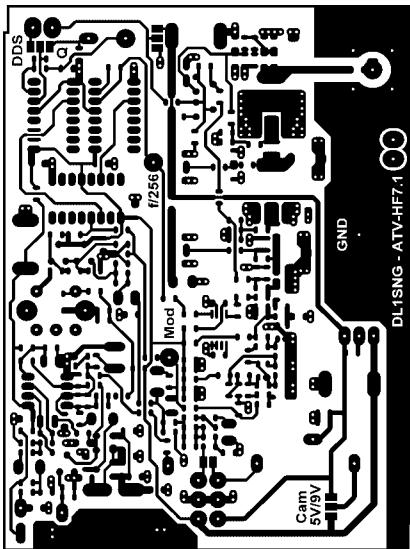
Layout der Platinenoberseite im Maßstab 1:1
